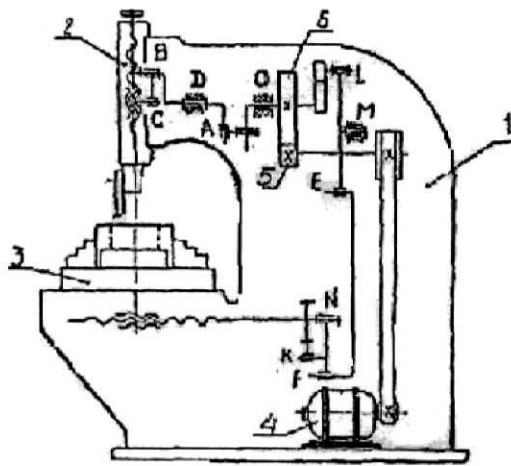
Общий вид долбежного станка с вращающейся кулисой
